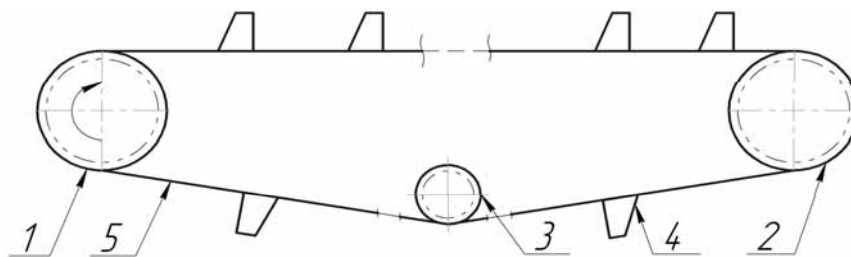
Схема режущего аппарата бесподпорного среза стеблей:
